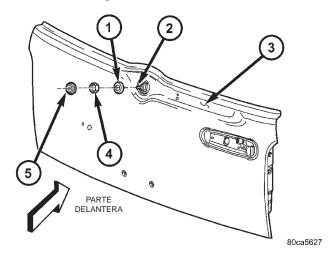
Desmontaje e instalación de la tuerca del eje transmisor del motor de limpiador trasero
